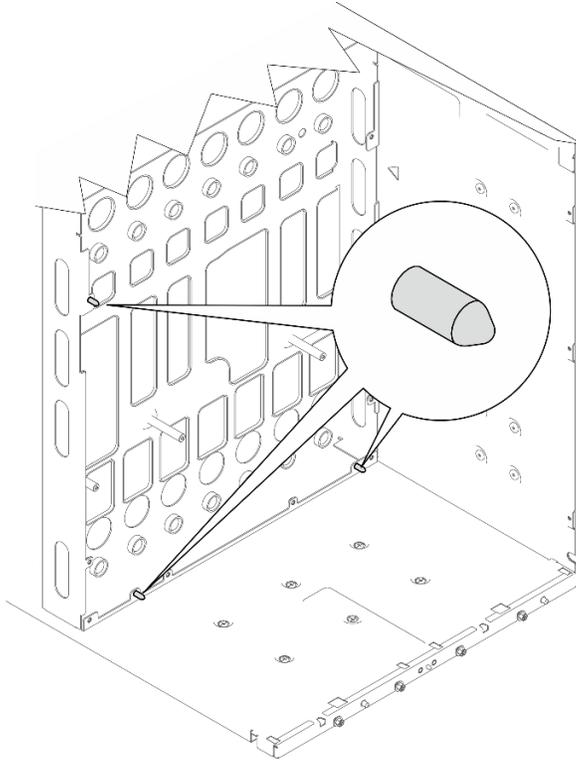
Broches de guidage pour l'installation de l'assemblage de la plaque médiane
